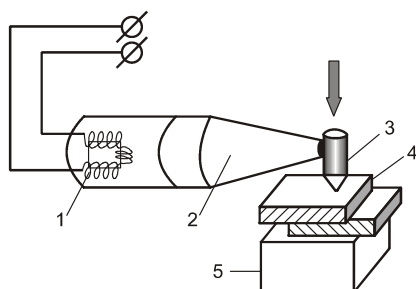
Ультразвуковой сварочный агрегат с концентратором: 1 — преобразователь; 2 — концентратор; 3 — ударник; 4 — свариваемые детали; 5 — подложка
